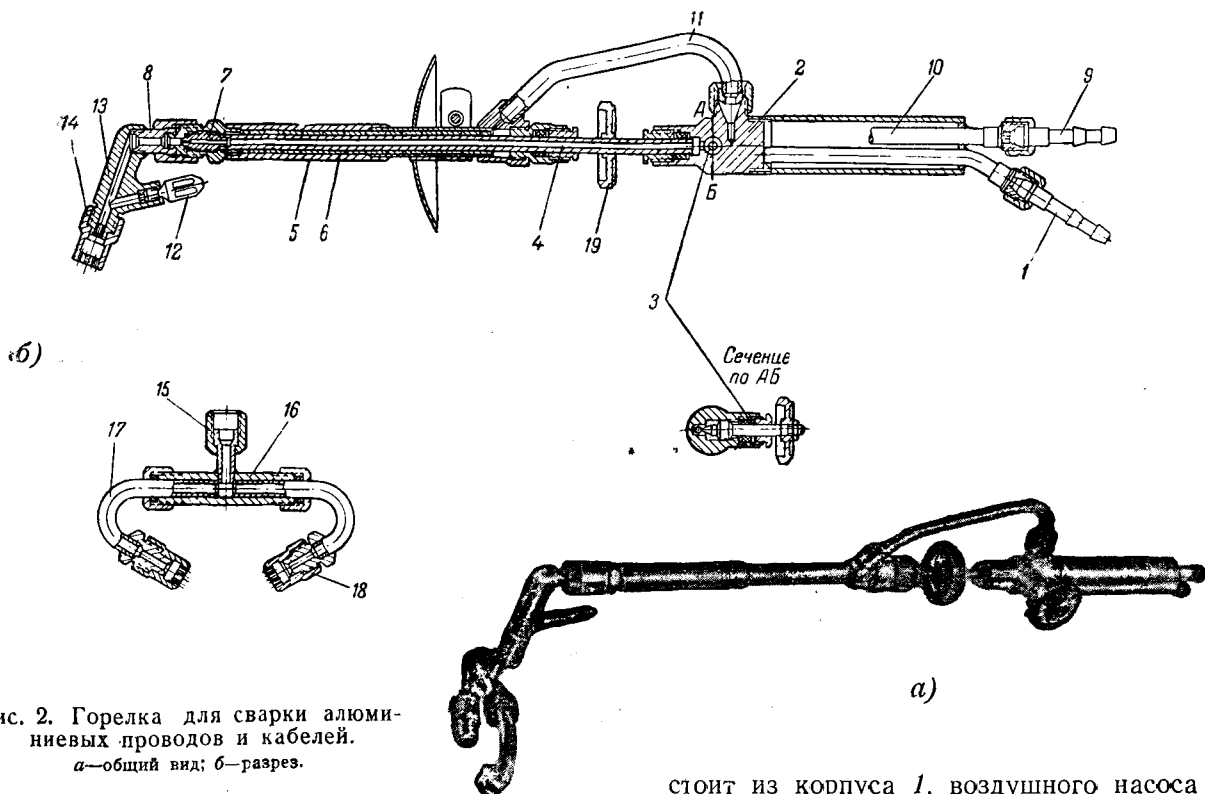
Горелка для сварки алюминиевых проводов и кабелей.
